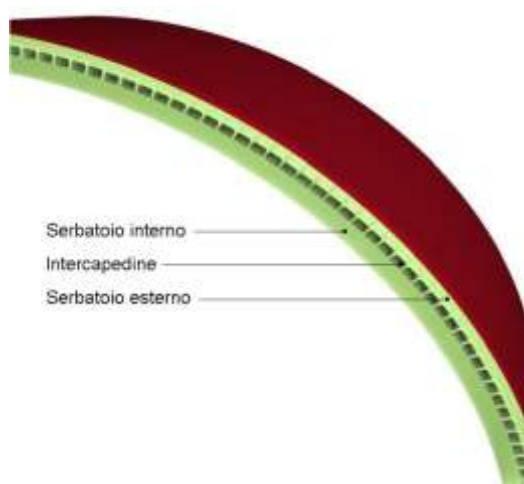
PARTICOLARE DI UNA STRUTTURA IN DOPPIA PARETE
